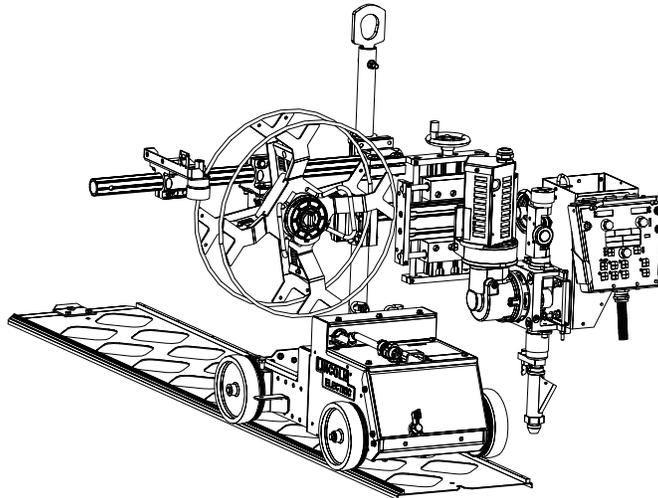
VISTA SUPERIOR DE LA SOLDADURA DE CARRIL
